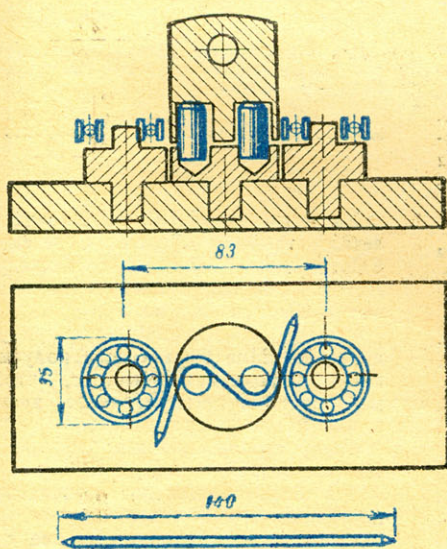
Гибочное приспособление для изготовления шипов конструкции Н. Закревского (сборочный чертеж).
